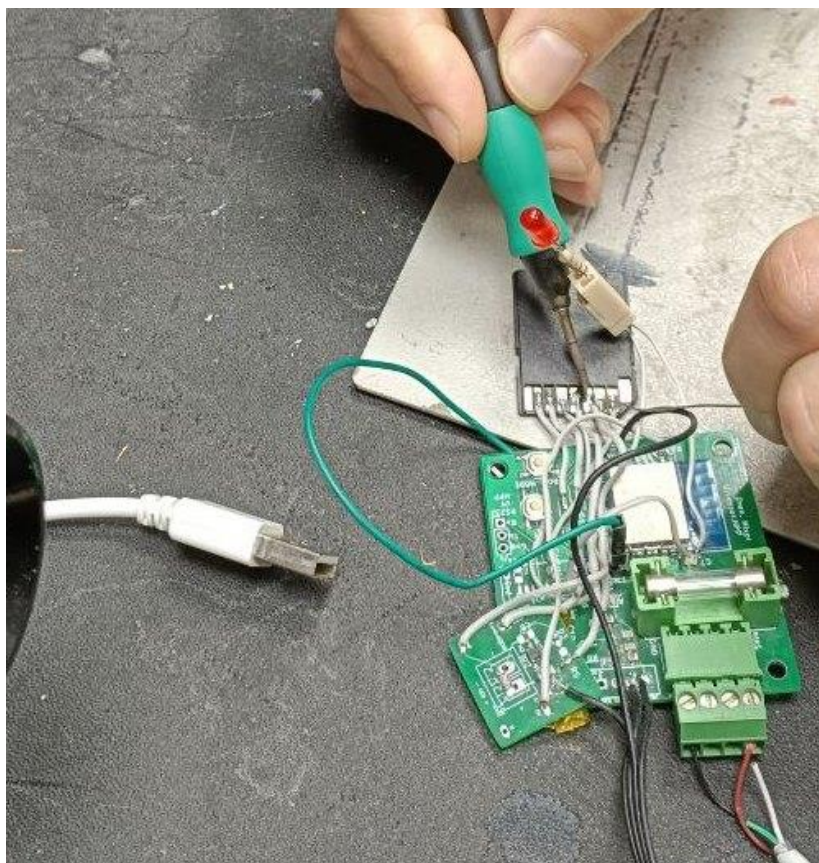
Comprobación de las soldaduras de una memoria microSD a una placa provisional de prueba.
